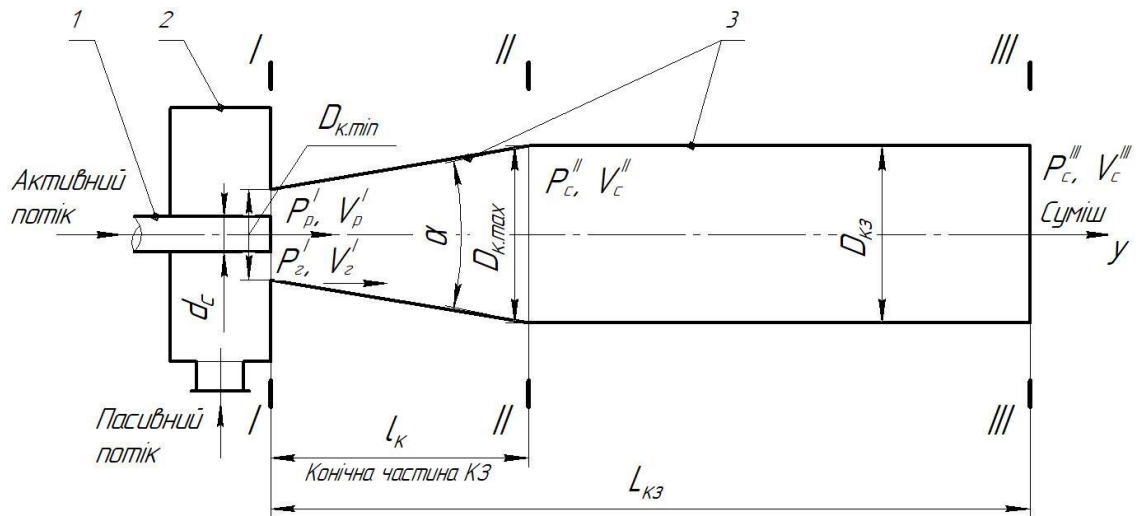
Розрахункова схема ежектора з конічно-циліндричною камерою змішування:
